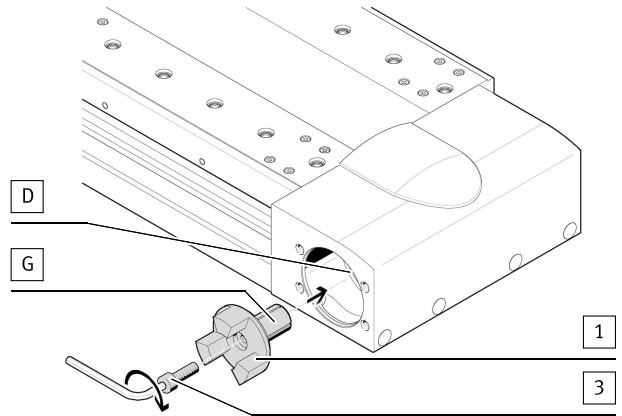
Крепление ступицы муфты, на стороне координатного привода
